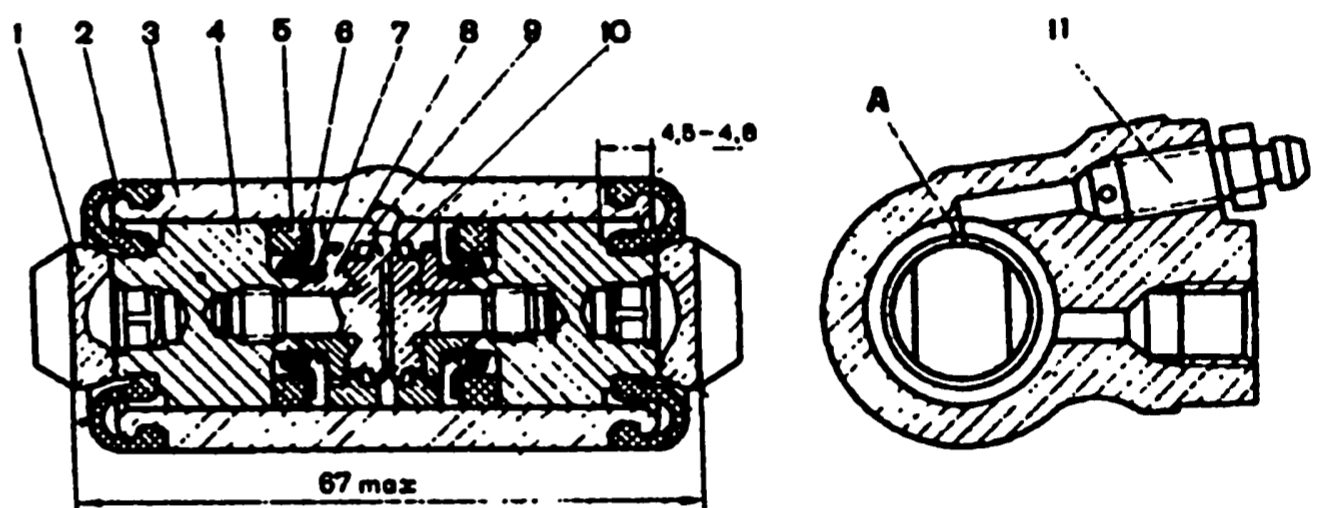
Колесный цилиндр: 1 - упор колодки; 2 - защитный колпачок; 3 - корпус цилиндра; 4 - поршень; 5 - уплотнитель; 6 - опорная чашка; 7 - пружина; 8 - сухари; 9 - упорное кольцо; 10 - упорный винт; 11 - штуцер; А - прорезь на упорном кольце
